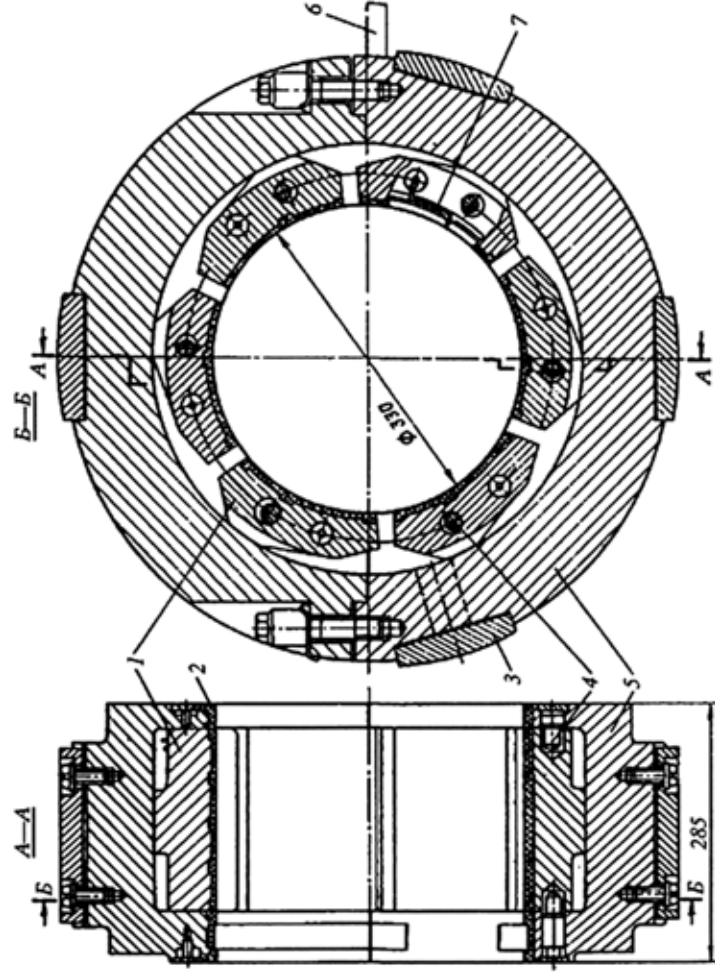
Сегментный подшипник конструкции ЛМЗ: 1 – сегменты; 2 – уплотнение; 3 – установочные колодки; 4 – штифты; 5 – вкладыш; 6 – стопорная шайба; 7 – термопласта
